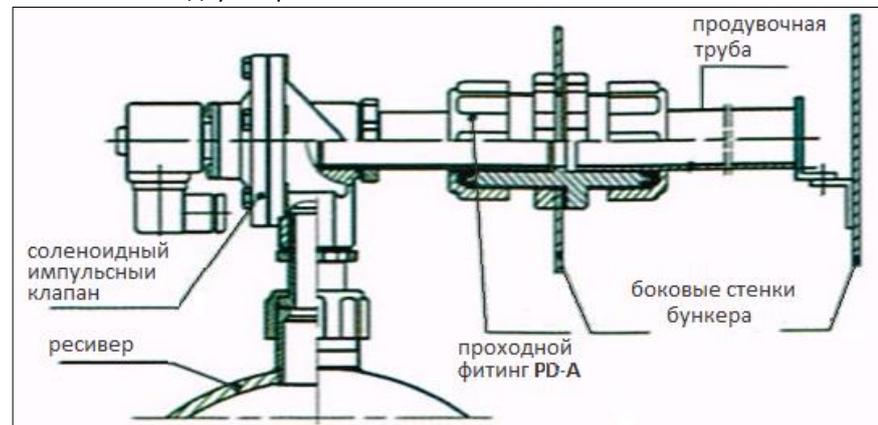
Монтажный чертёж установки проходного двухстороннего фитинга PD-A
